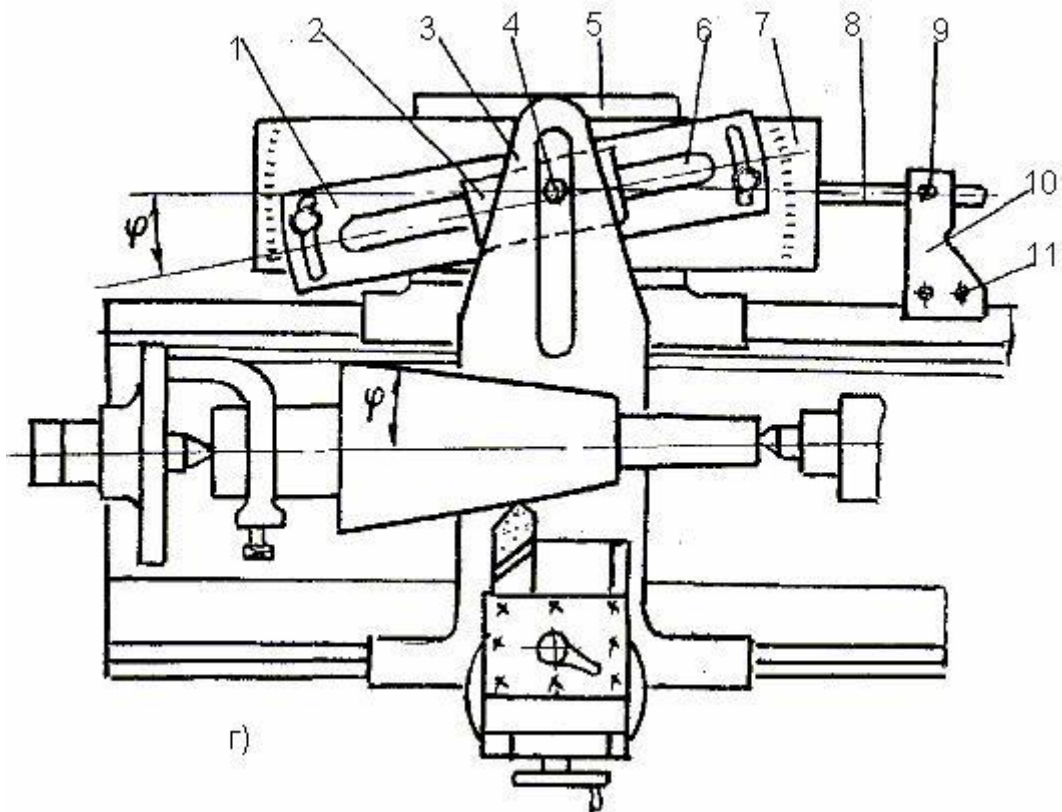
Схеми обробки конічних поверхонь на токарних верстатах
